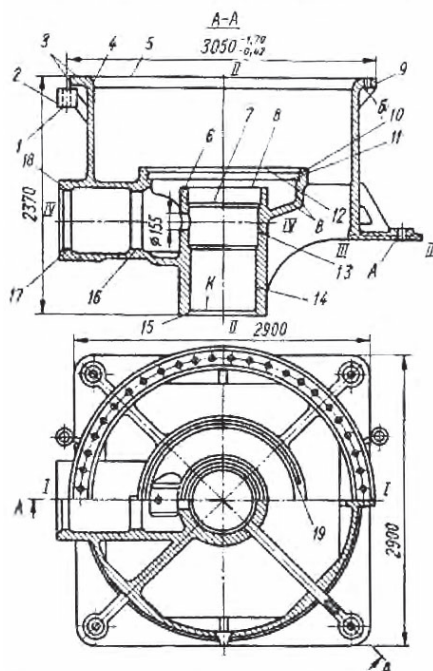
Станина конусної дробарки 2100 для середнього дроблення
